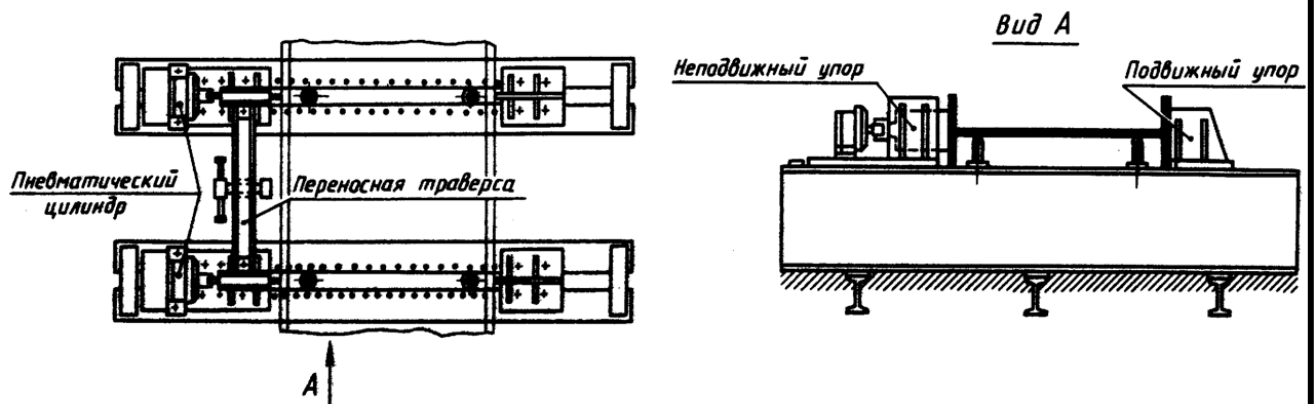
Універсальний складальний кондуктор с пневматичними притискачами
